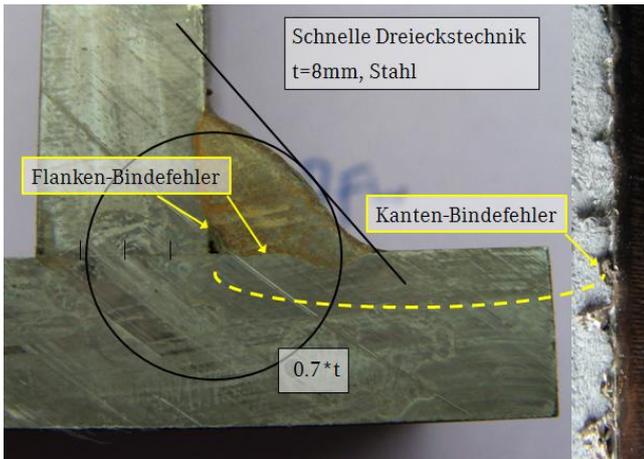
Steignaht zu hastig geschweißt, Bindefehler im Bruch und Schliff erkennbar (Stahl 8mm, M21, 1mm G3Si1)
